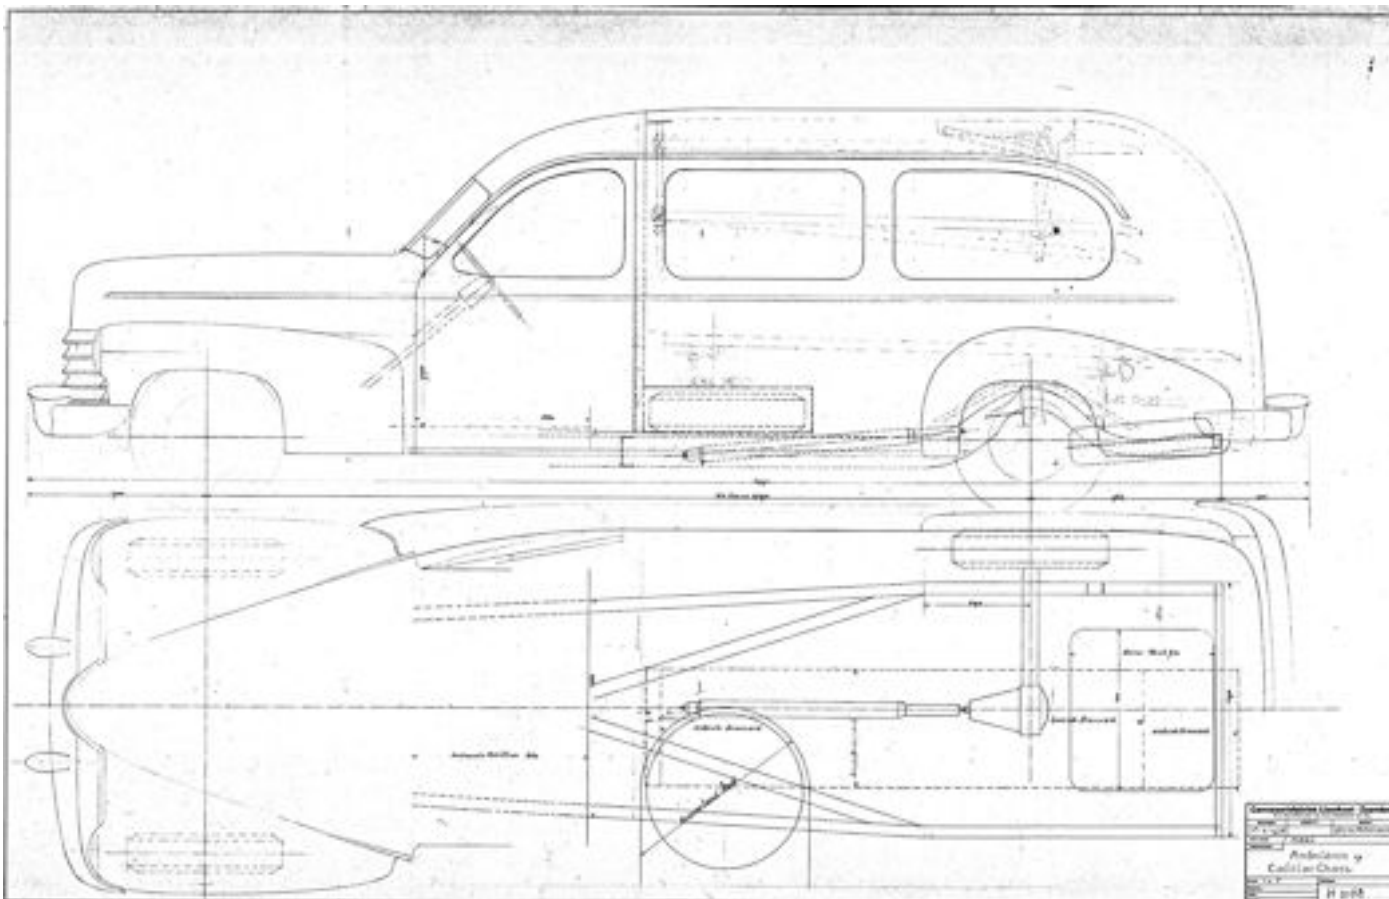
Een ontwerptekening van Johan Ankel (N.V. Wagenbouw 'Holland-ambulance') voor een ziekenauto op basis van een Cadillac Fleetwood 1947 voor de GGD Hilversum (bron: coll. Hans Waldeck, De Wijk).
